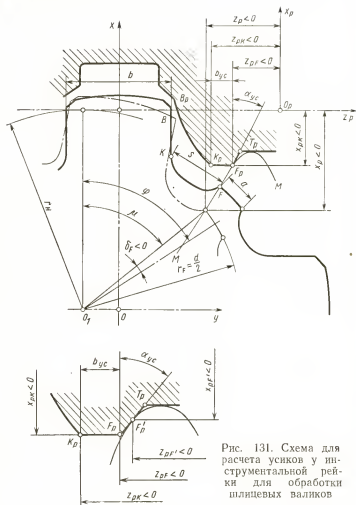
Схема для расчета усов у инструментальной рейки для обработки шлицевых валиков
